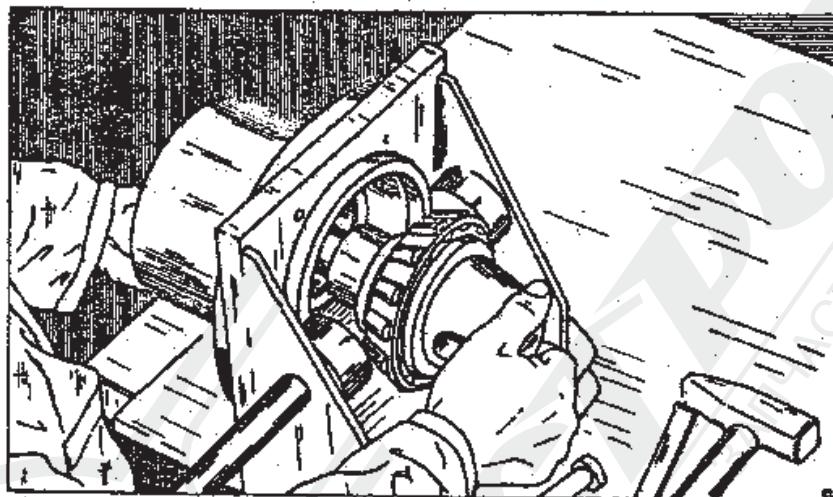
Крепление конического роликоподшипника со стержнем прибора.
